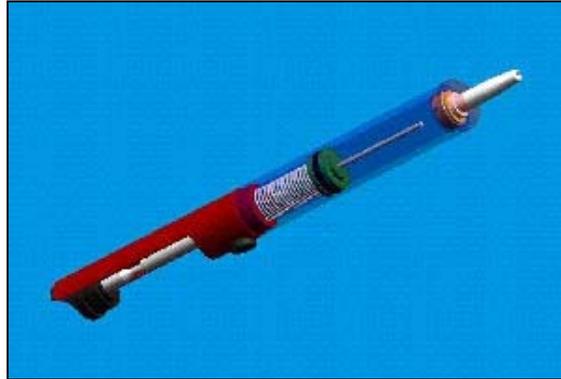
Desoldador, por Carrillo, Patricio y Fermosell, Fernando
